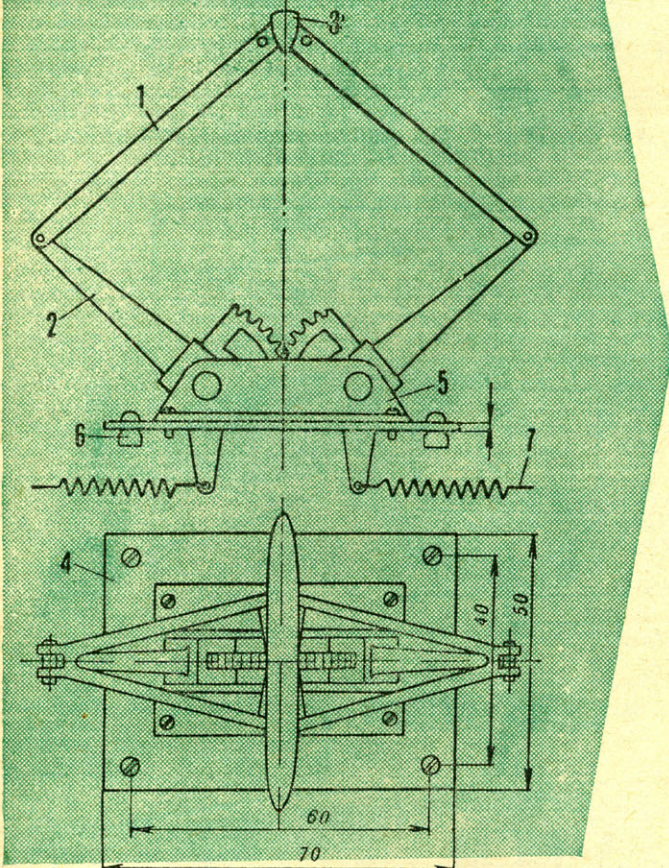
Детали пантографа: 1 — верхний рычаг, 2 — нижний рычаг, 3 — валин для шарнира нижнего рычага, 4 — контактный башман, 5 — основание контактного башмана, 6 — шпилька для соединения с рычагами.
